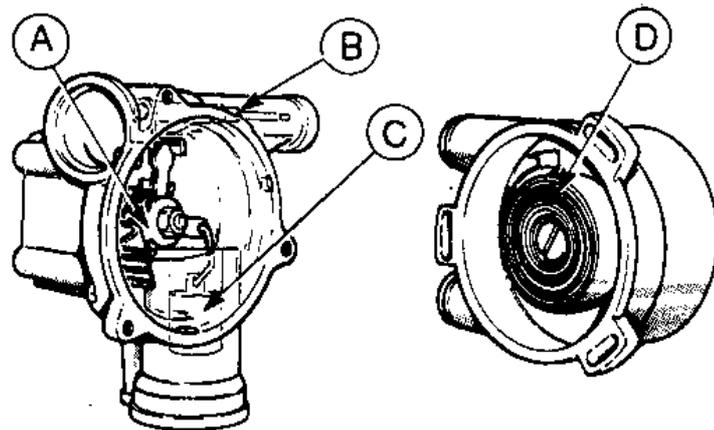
Автоматическая система пуска и прогрева двигателя (Разд.25)
